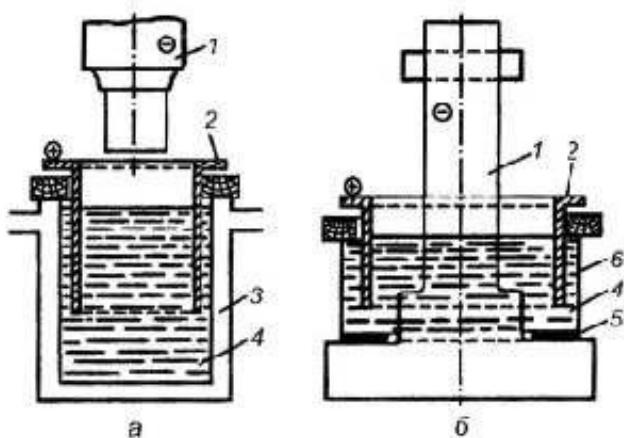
Конструктивные схемы ванн для хромирования крупных деталей: а — передвижной; б — накладной; 1 — деталь (катод); 2 — анод; 3 — ванна с двойными стенками; 4 — электролит; 5 — уплотнение; 6 — ванна
